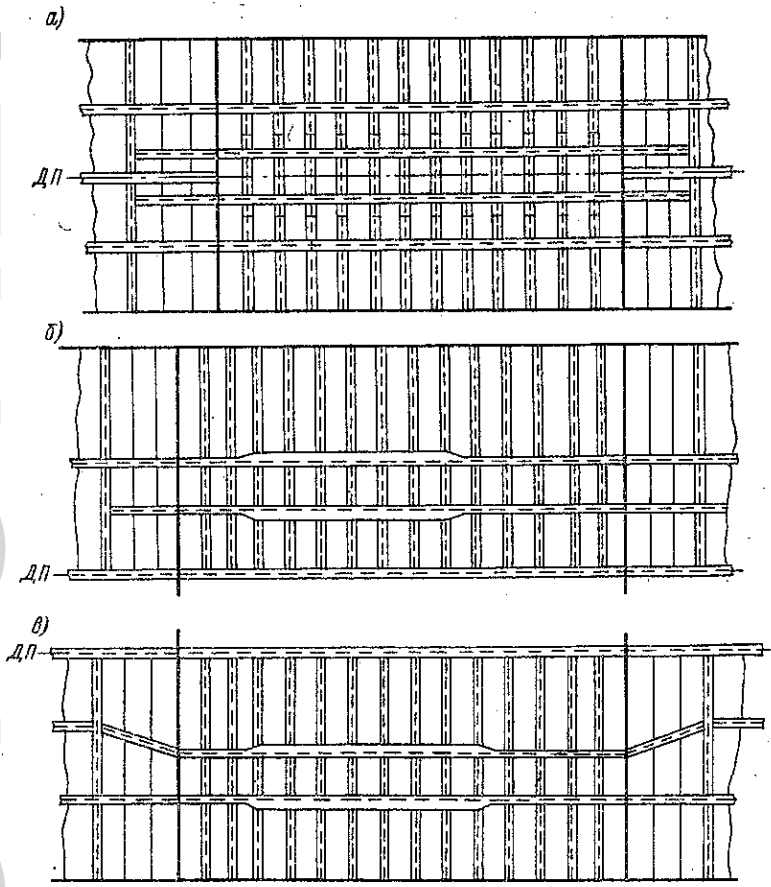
Схемы конструкции днищевое перекрытия машинного отделения
